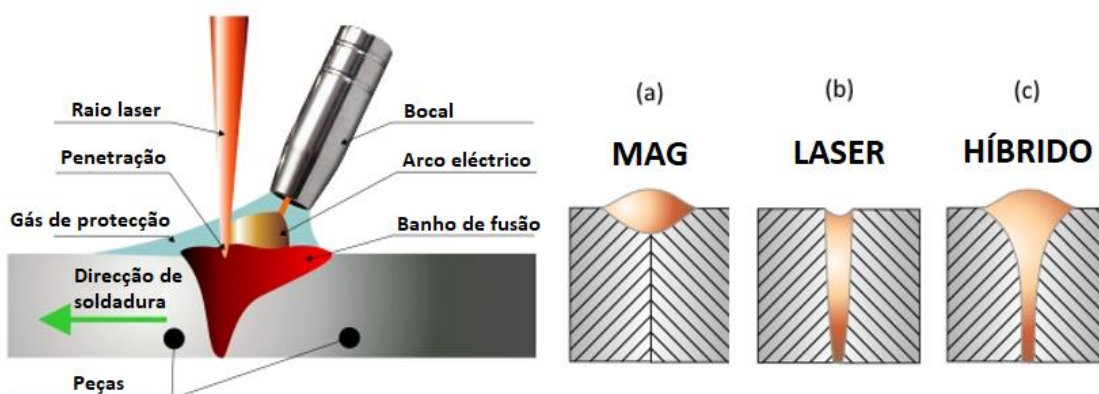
Comparação dos resultados dos diferentes processos de soldadura: a) Soldadura MAG, b) Soldadura Laser, c) Soldadura Híbrida [Adaptado de (EAGLE)].
